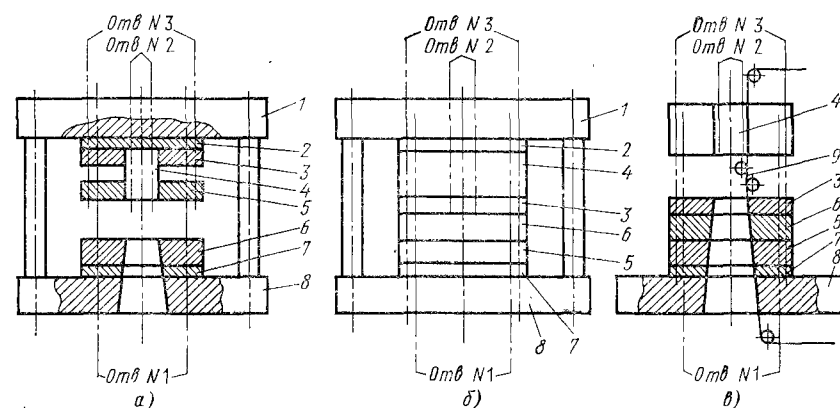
Вырубной штамп простого действия (а), сборка заготовок его основных деталей (б) и схема их обработки (в)
